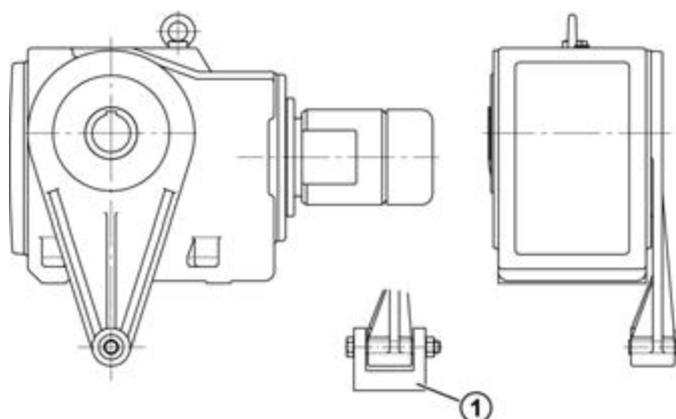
Резиновые амортизаторы (опция G или VG) на редукторах с параллельными валами
